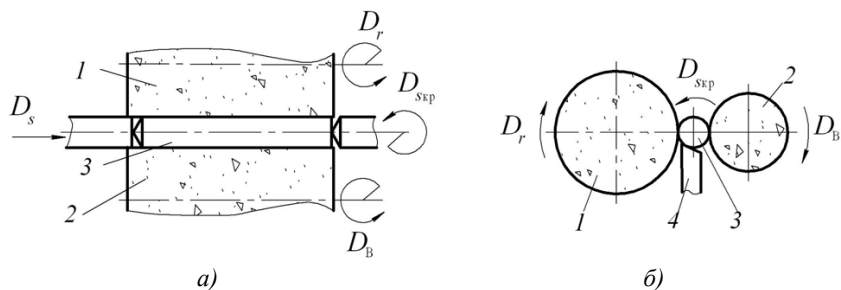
Шлифование на бесцентровошлифовальном станке с продольной подачей: 1 – рабочий круг; 2 – ведущий круг; 3 – заготовка; 4 – опорный нож
